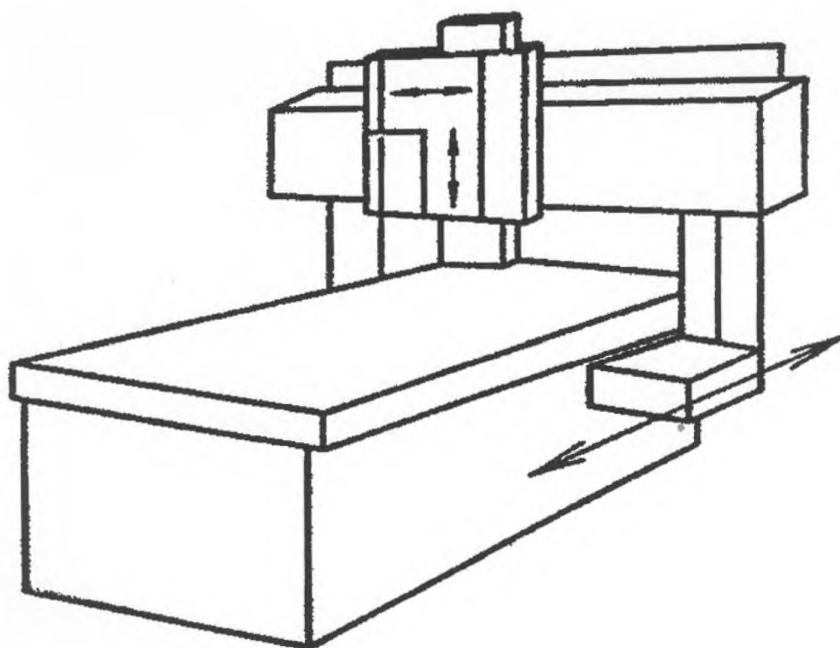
Фрезерный станок с верхним расположением шпинделя (неподвижный стол, подвижный портал, подвижная головка)¹
